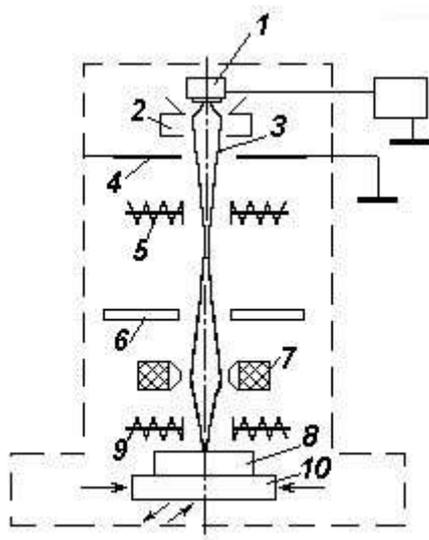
Схема электронно-лучевой сварки
